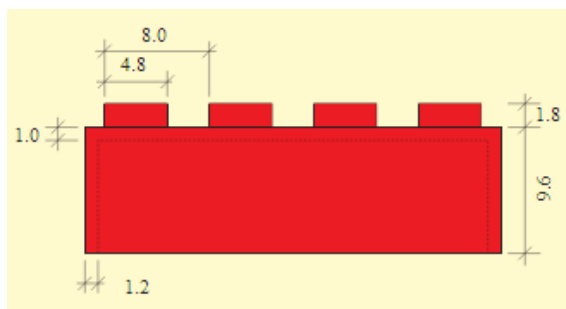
Vista lateral izquierda de una pieza de LEGO 4 x 2, [6]
